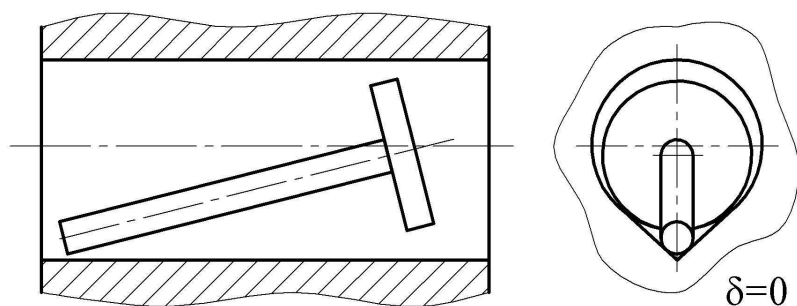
Базирование типовой стержневой детали в призматическом отверстии
